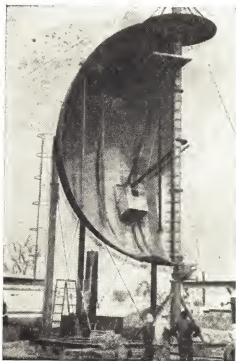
Сварка шарового резервуара без его вращения. Сварочный автомат варит шов снаружи «шарнира».
